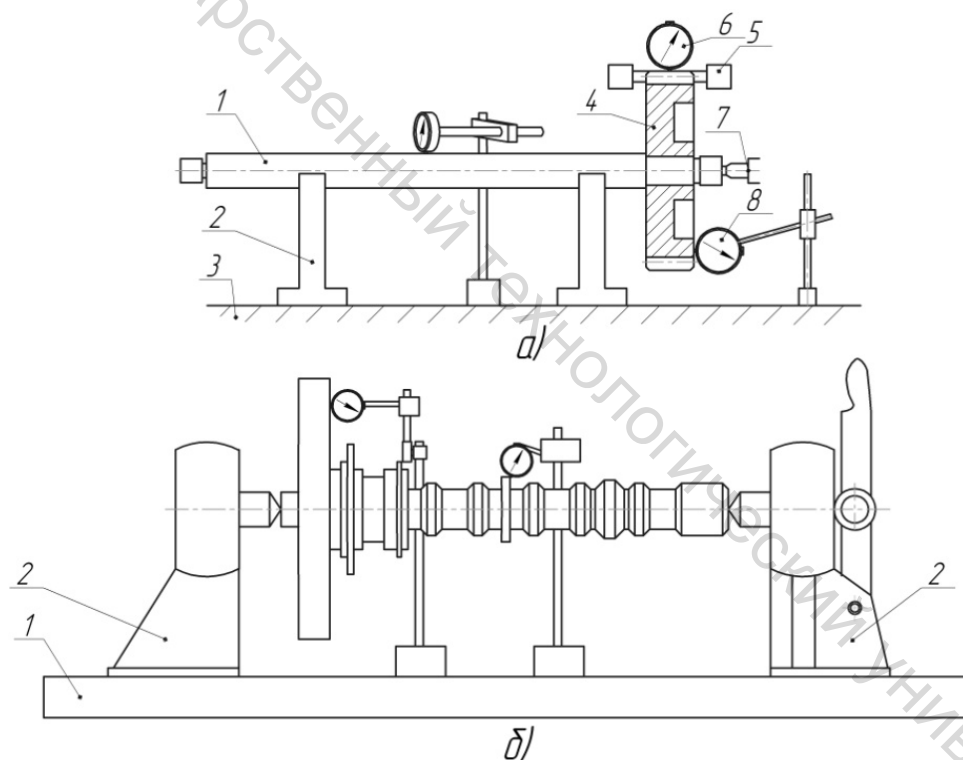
Контроль на биение узла «зубчатое колесо – вал»:
